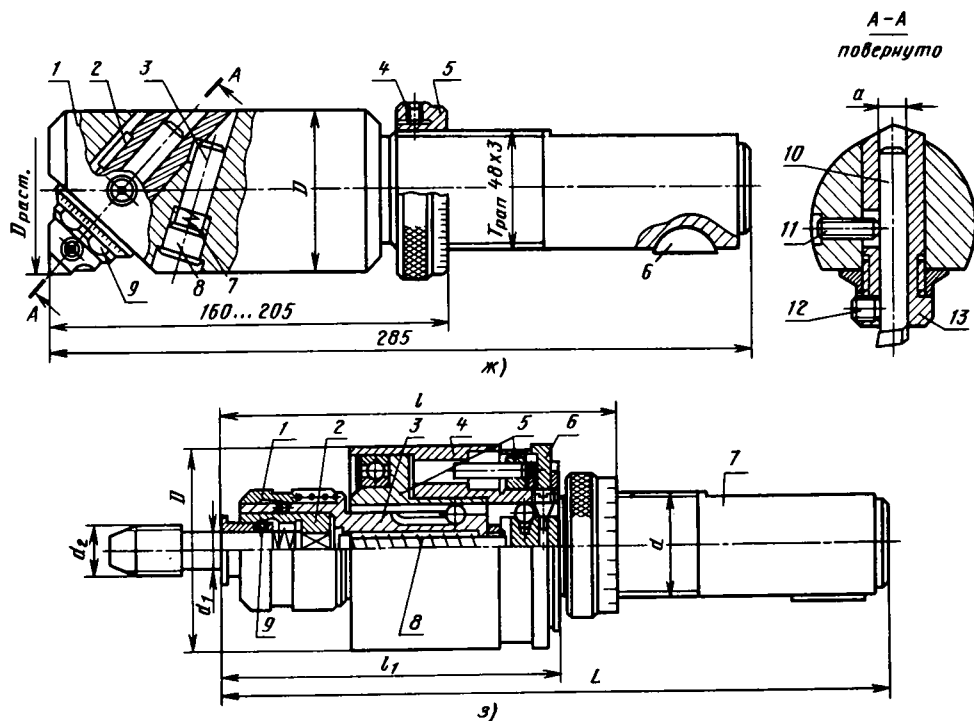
Инструменты и инструментальные блоки станков с ЧПУ сверлильно-расточной и фрезерной групп:
